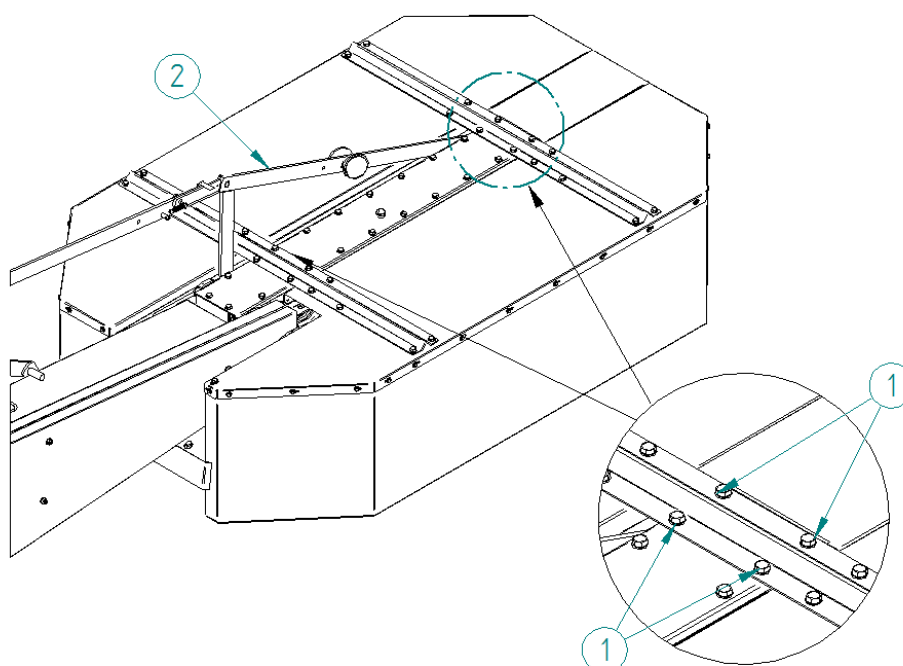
Montaggio sezioni metalliche / Metal guard assembly
